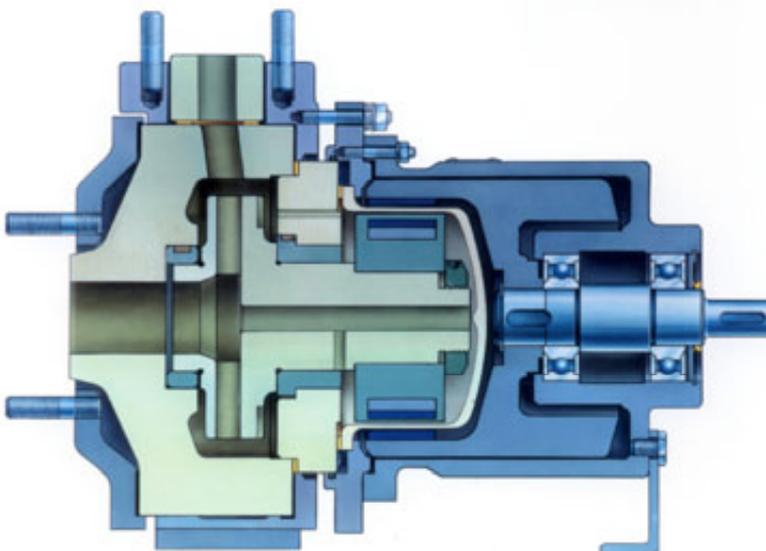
Ein High-Tec-Produkt der Rheinhütte: Eine hermetisch dichte Keramikpumpe. (Frikotherm® B). Patentiertes Laufrad mit Welle und Aufnahme für Magnetkuppelungs-Innenteil aus einem Stück. Die Pumpe ist geeignet zu Förderung von hochtoxischen, hochkorrosiven und aggressiven Medien bis 200 °C.
